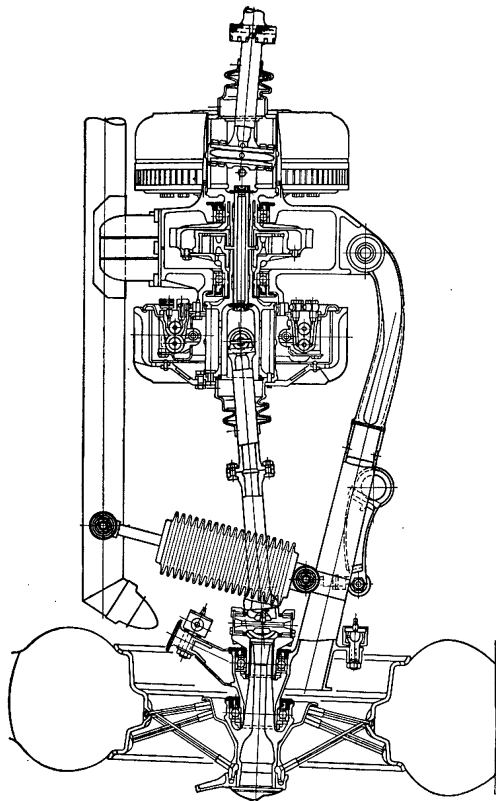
Конструкция подвески задних колес автомобиля «Мерседес-Бенц»
